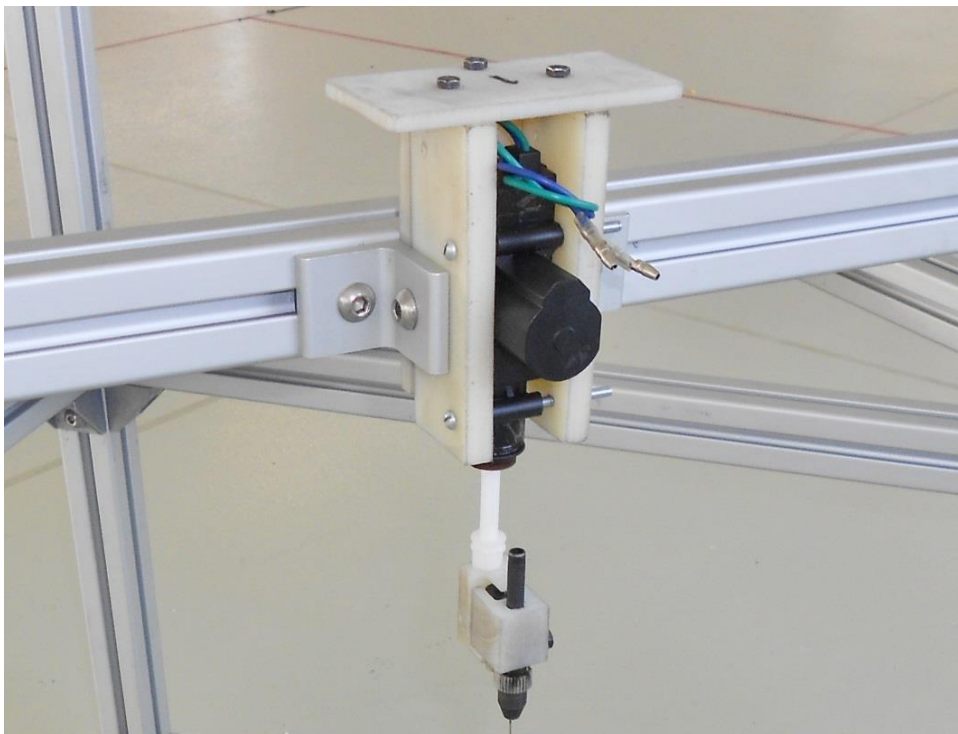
Mecanismo superior del sistema de Inserción de hilo ensamblado en el prototipo de máquina bordadora.
